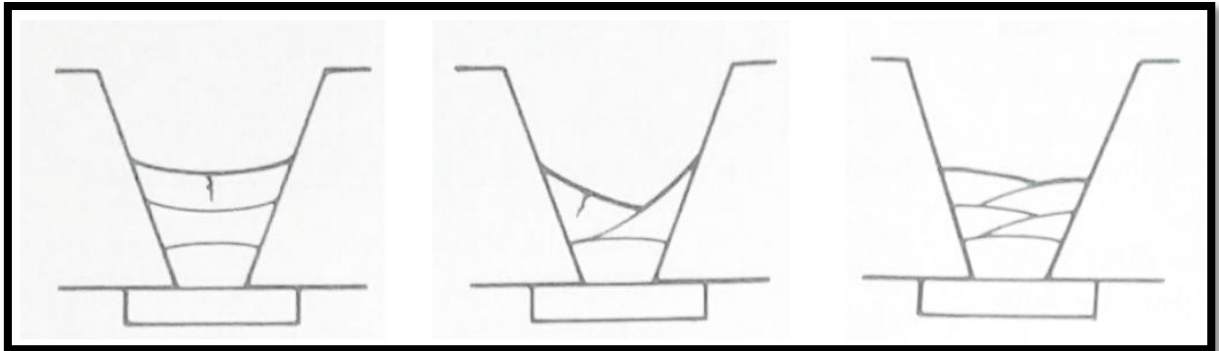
Trincas no cordão de solda durante os passos do processo de soldagem. Fonte: AWS D1.1(2004)
